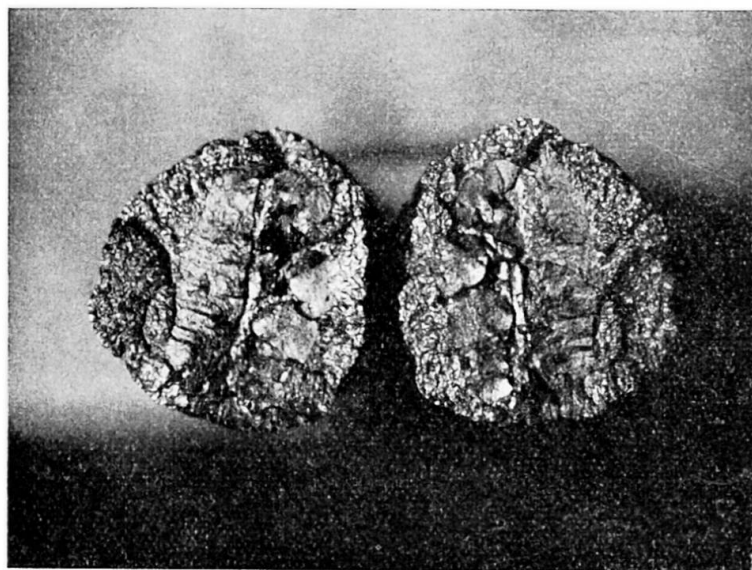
Rupture par fatigue d'une soudure présentant un défaut d'angle.
